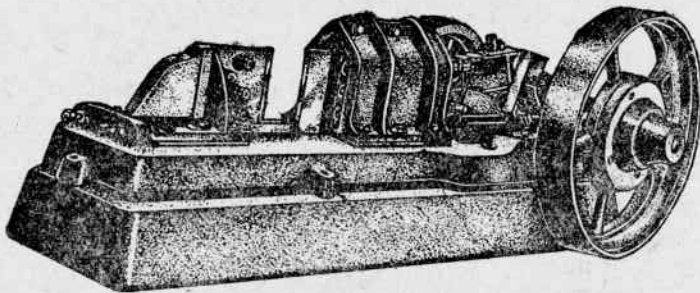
Станок для дробления реек, корней и сучьев, идущих на перегуливание.
